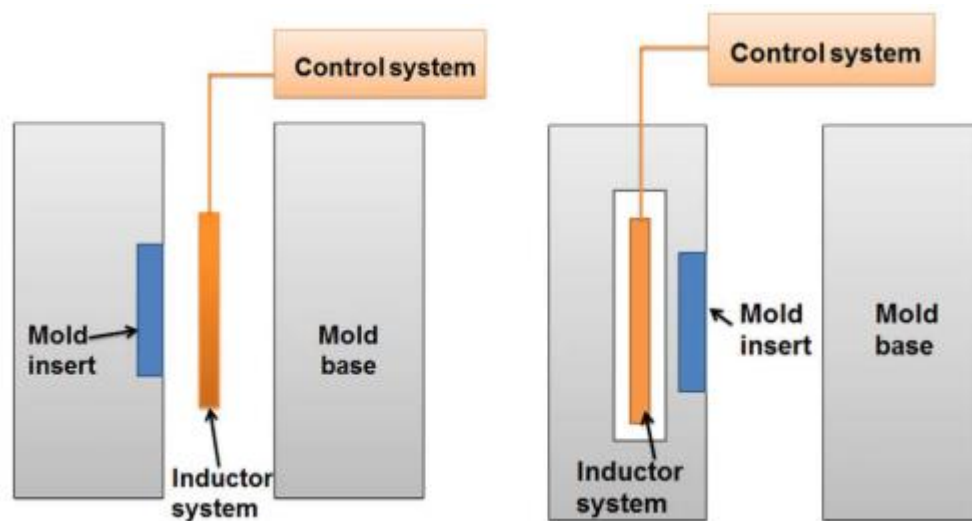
Esquema de aquecimento por indução externa e interna. Esquerda: sistema externo para aquecimento por indução; direita: integração de um indutor num inserto do molde [29].
